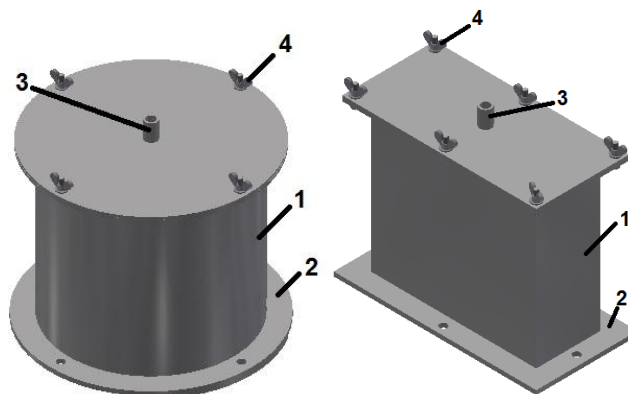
Los moldes y sus partes. Molde cilíndrico (izquierda), Molde prismático rectangular (derecha).
